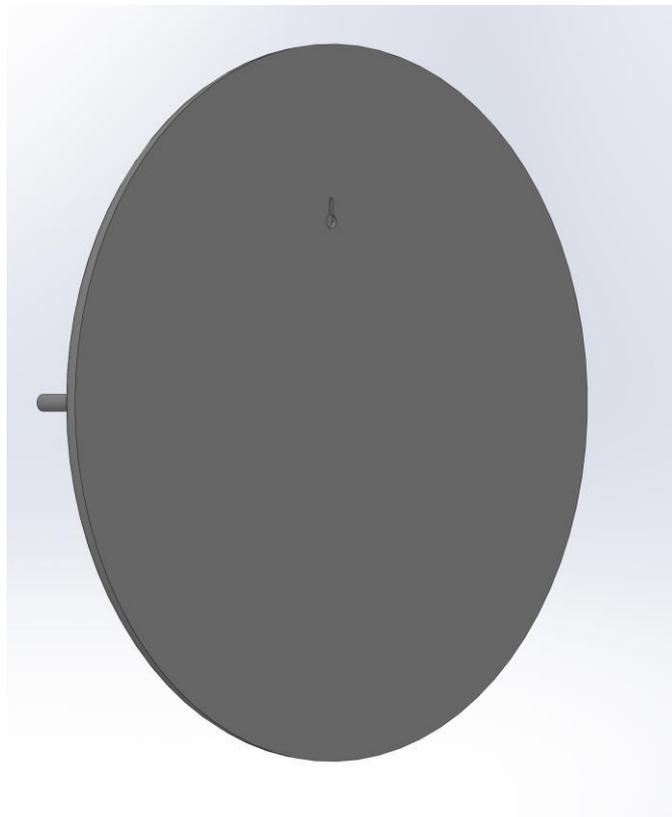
Modelagem do suporte de fixação. Fonte: Elaboração própria
